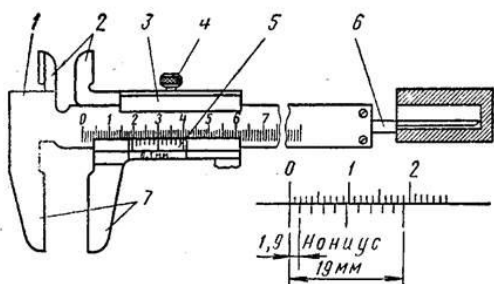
Штангенциркуль ШЦ – I. 1 — штанга, 2, 7 — губки, 3 — подвижная рамка, 4 — зажим, 5 — шкала нониуса, 6 — линейка глубиномера
